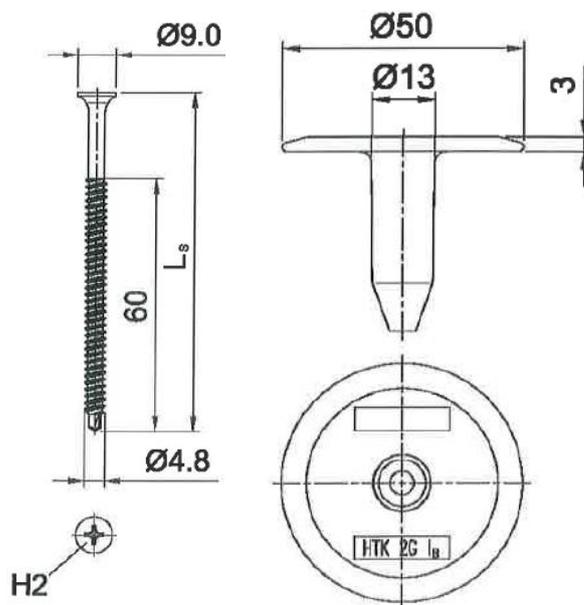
Vis ETANCO EHB DF-2C 4.8+ plaquette de fixation ETANCO DVP DF 8240R
